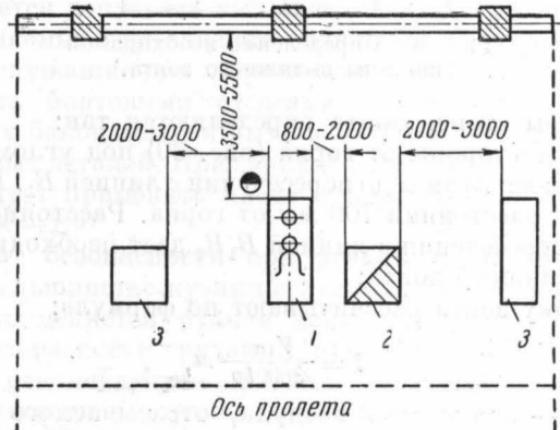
Схема расположения ковочного пневматического молота и печи:
